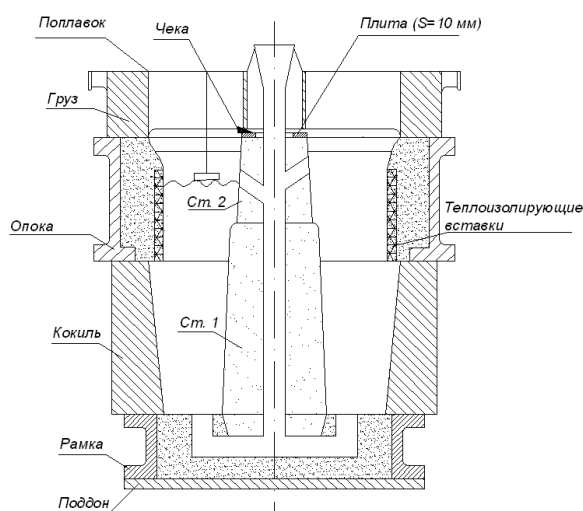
Схема форма в сборе отливки «бандаж» из стали 150ХНМЛ.
